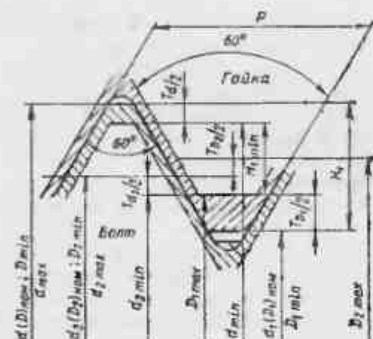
Расположение полей допусков метрической резьбы при посадке с наименьшим зазором, равным нулю
